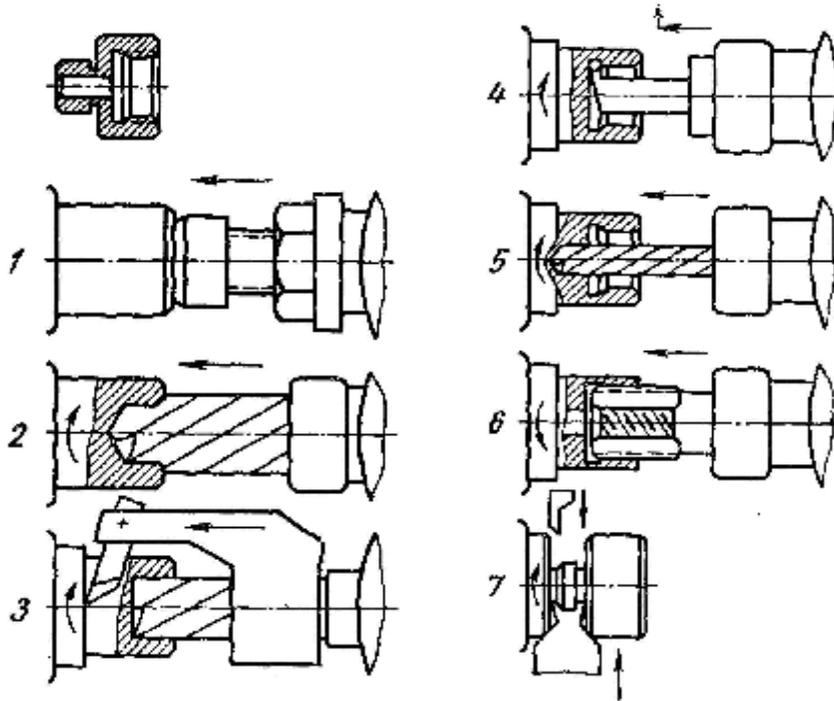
План (последовательность) обработки детали на токарно-револьверном автомате с использованием поперечных и револьверного суппортов
